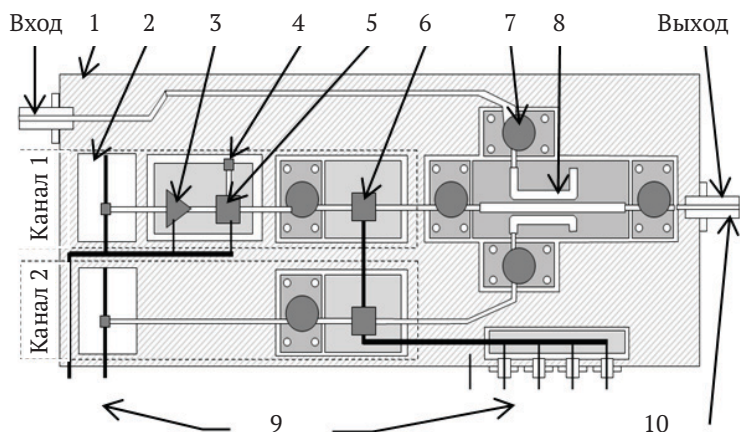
Конструкция микросборки БГШ диапазона 18-21 см: 1 – герметичный корпус; 2 – генератор шума на лавинно-пролетных диодах; 3 – усилитель шумового сигнала; 4 – нагрузка согласованная; 5 – переключатель; 6 – широкополосный управляемый напряжением рi-n-аттенюатор; 7 – развязывающий ферритовый вентиль; 8 – двухплечевой направленный ответвитель; 9 – изолированные штыри для подачи питания и управления; 10 – СВЧ-разъем с фланцем
